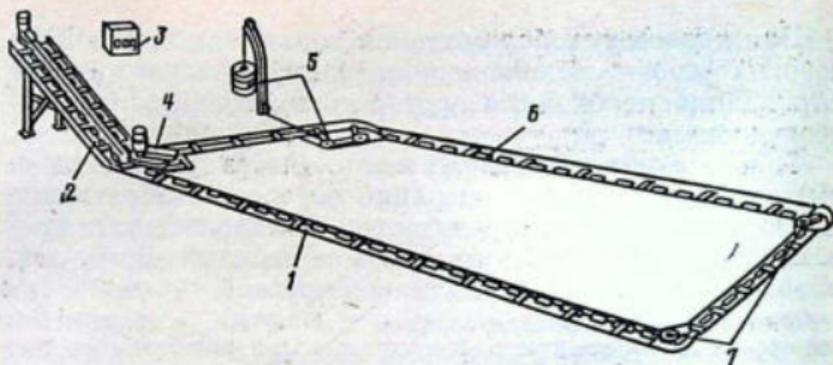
Скребокый навозоуборочный транспортер ТСН-160А:
